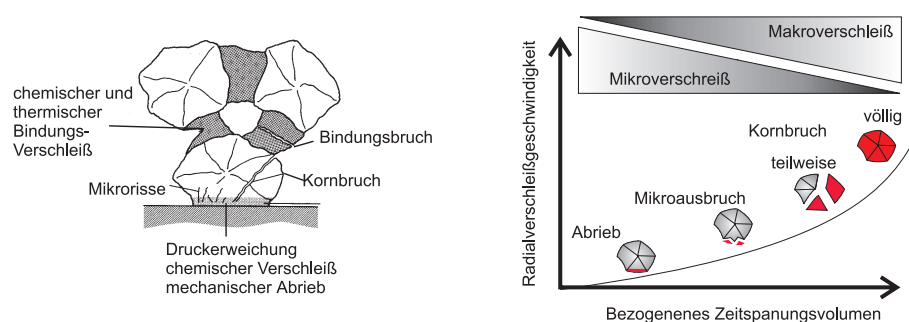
Verschleiß eines Werkzeuges auf Korn- und Werkzeugebene [88].
